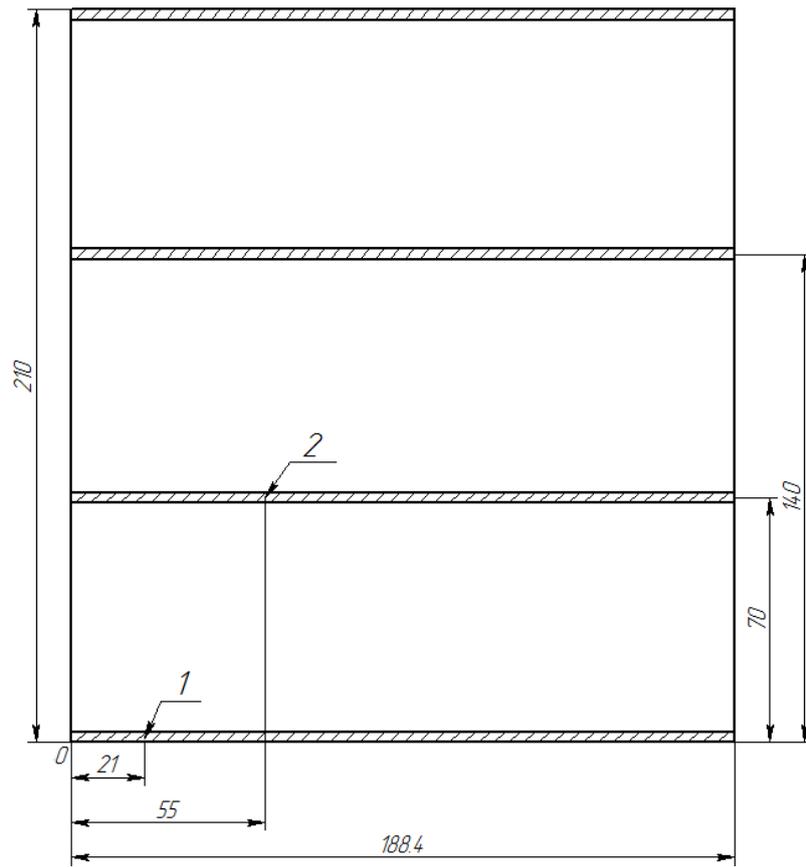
Развертка ОК с указанием местоположений дефектов.
